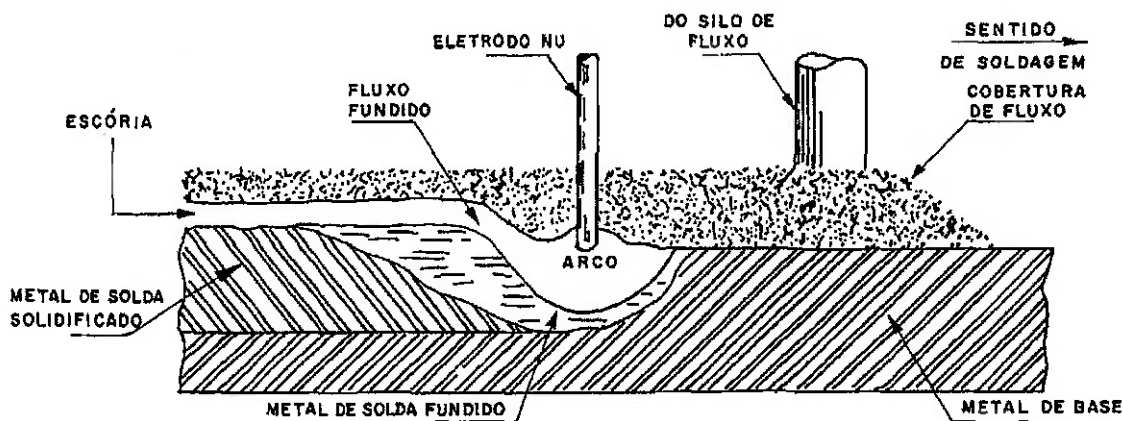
Esquema do processo de soldagem com arco submerso [5].
